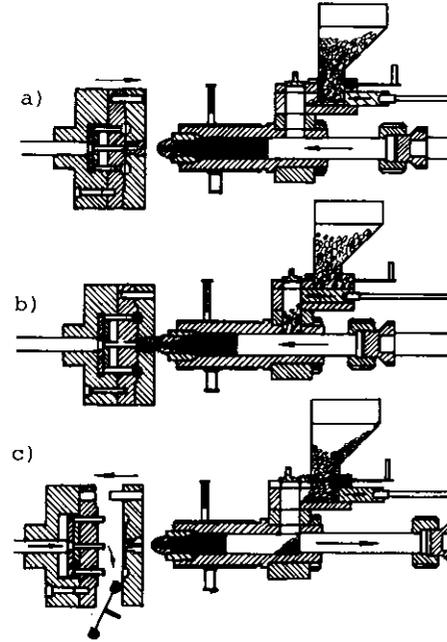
Seqüência de operações no processo de moldagem por injeção, em máquina de êmbolo. a) Fechamento do molde e aproximação da tubeira, com compressão simultânea do material plastificado; b) Injeção e, simultaneamente, dosagem do granulado para a próxima carga; c) Retorno do êmbolo com deslizamento do material granulado antes do dosado, desprendimento do massalote da tubeira e abertura do molde, e expulsão da peça.
